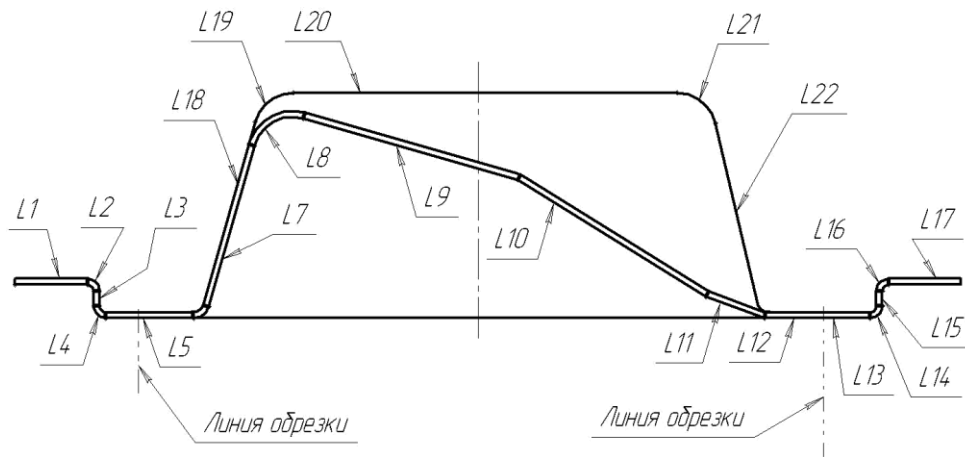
Наибольшее продольное сечение вытяжного перехода
